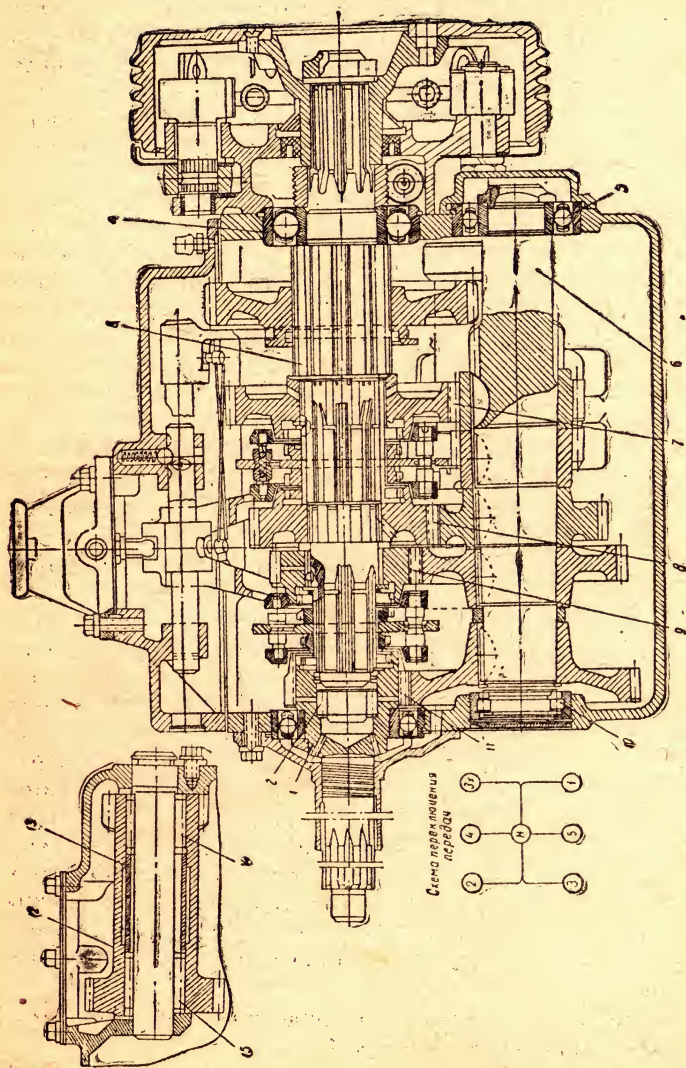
Коробка передач автомобиля ЗИЛ-130
